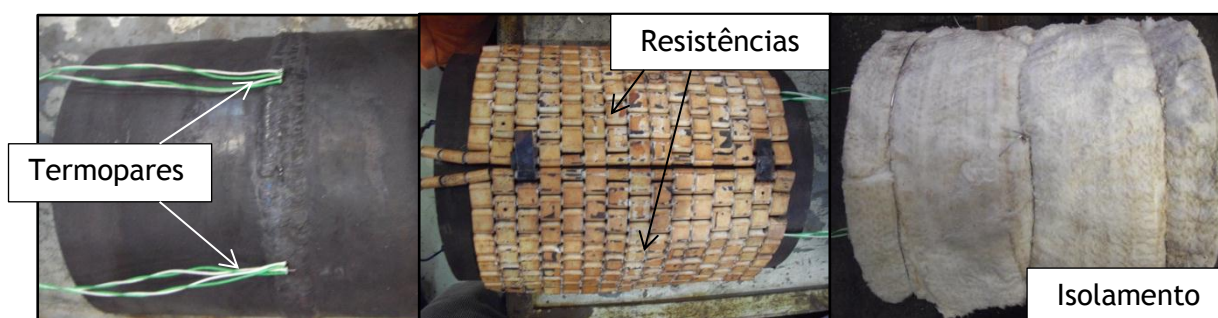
Montagem de parte de tubo para tratamento térmico após soldadura
